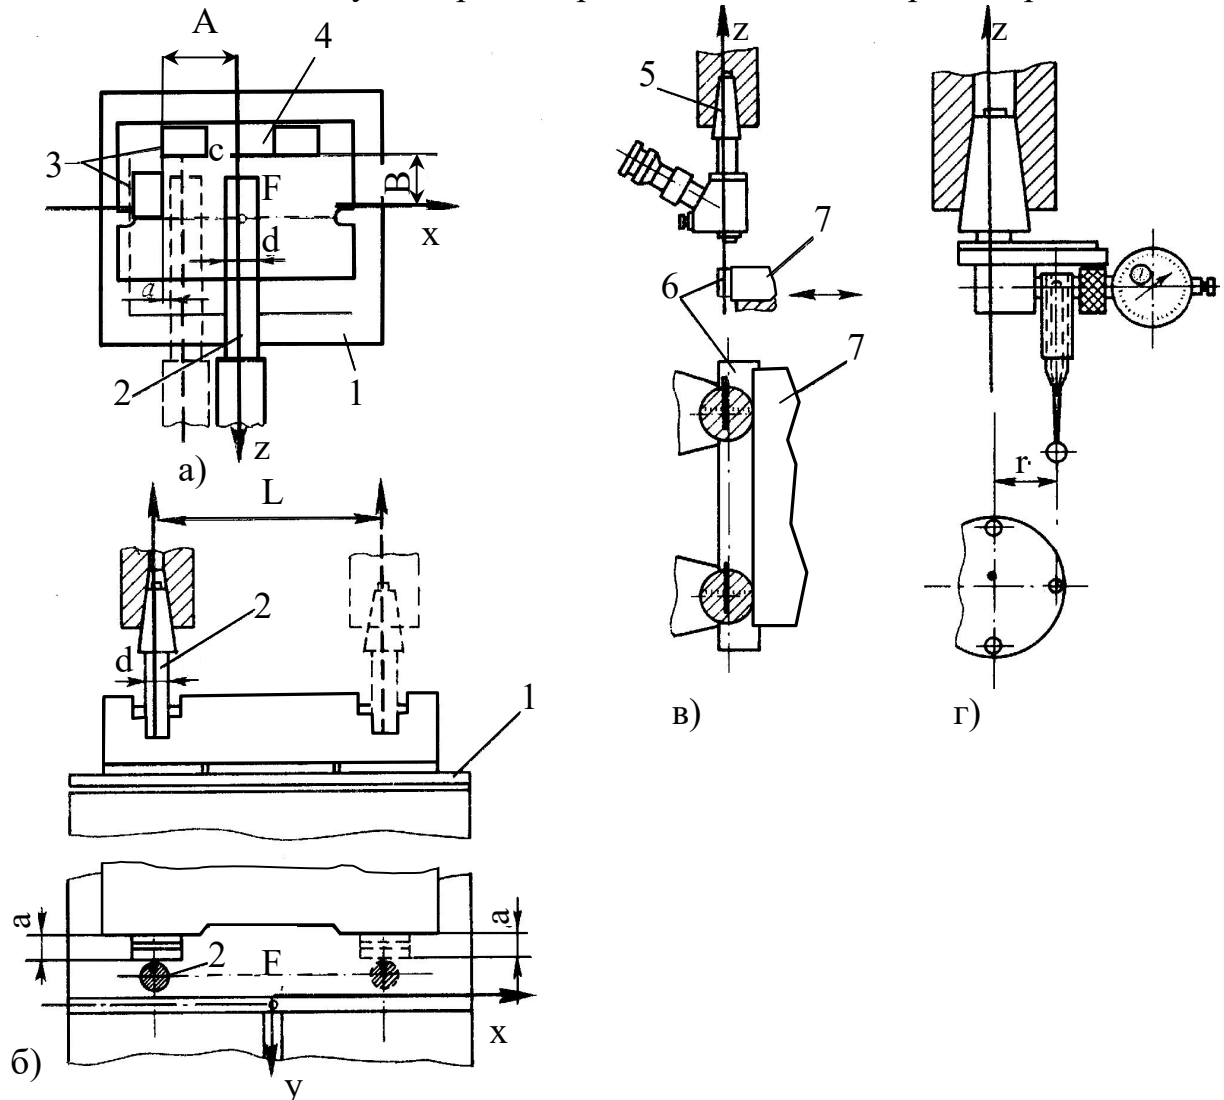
Схеми вивірення положення заготовок та пристосувань на столі верстата з ЧПК відносно осі його шпинделя: а, б – за допомогою мірних оправки та пластин; в, г – з використанням центрошукача (в – оптичного; г – індикаторного)
